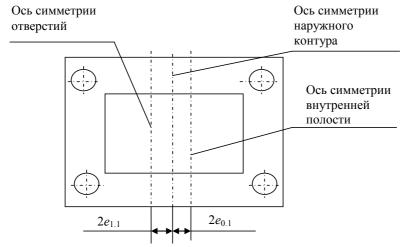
Смещение осей в заготовке и при обработке детали
